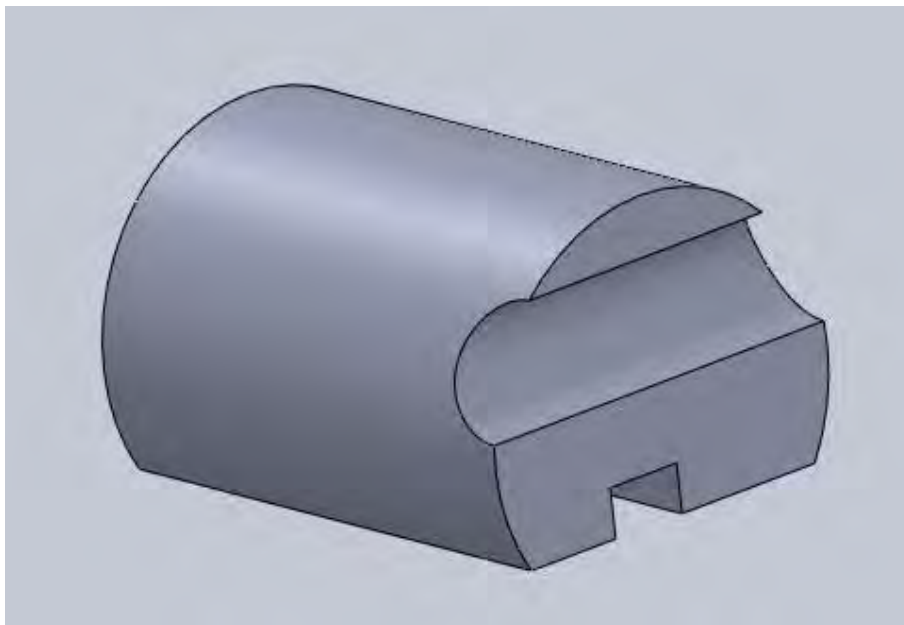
Diseño de opresor de tubo para dados de 19 mm hecho en SolidWorks.
